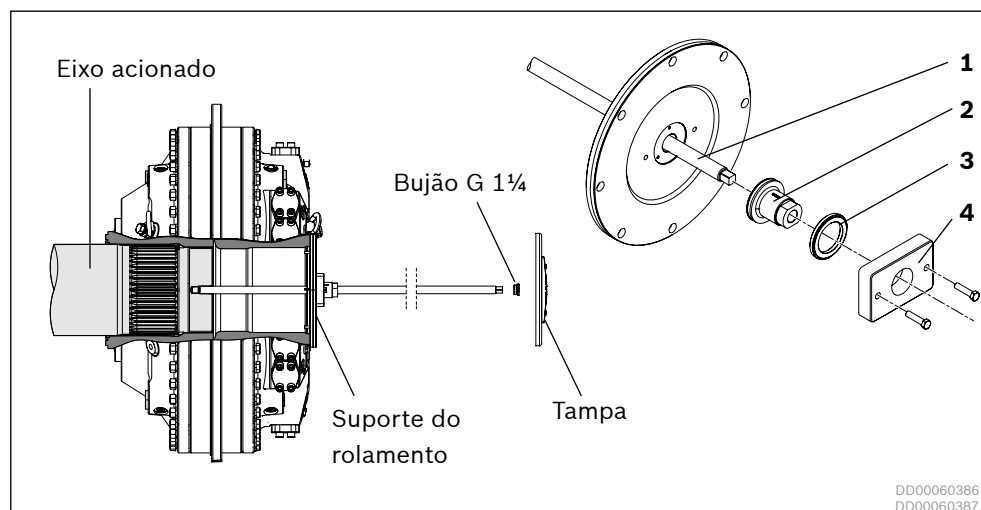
Ferramenta de montagem para a remoção do motor CBm com estria
